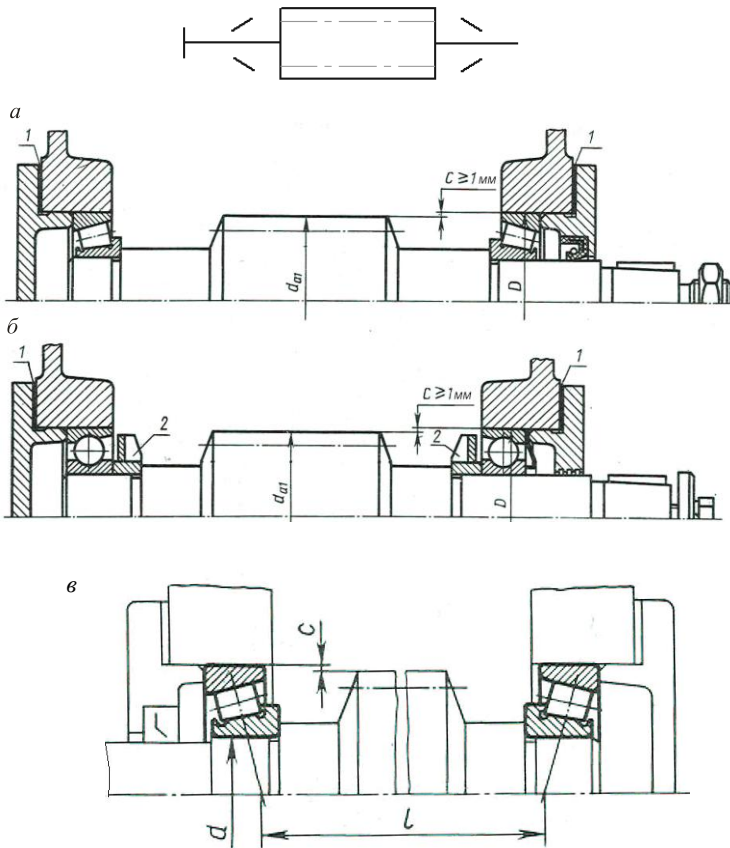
Схема установки подшипников «враспор» без плавающей опоры
